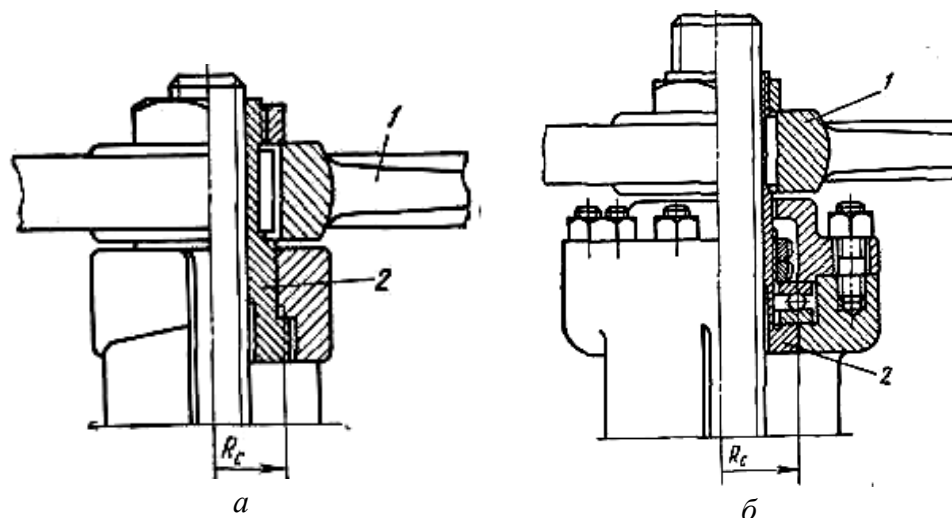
Опора втулки маховика: а – скольжения; б – качения
